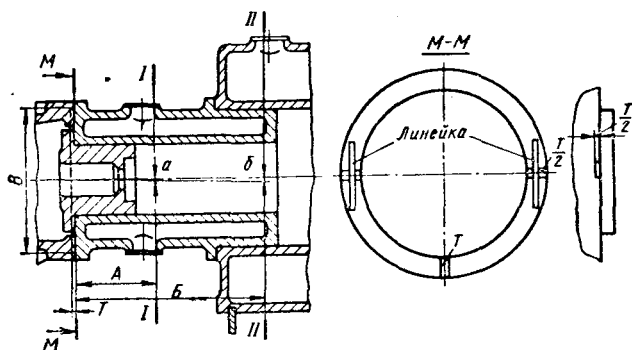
Схема проведения опиловки торца цилиндра для устранения излома осей
